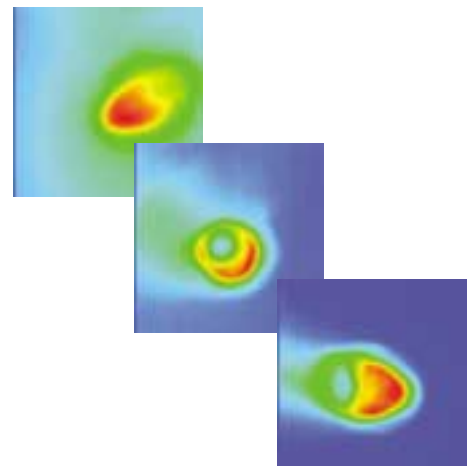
Prozessaufnahmen beim Schweißen einer 30°-Ecke, $v = 6 \text{ m / min}$
